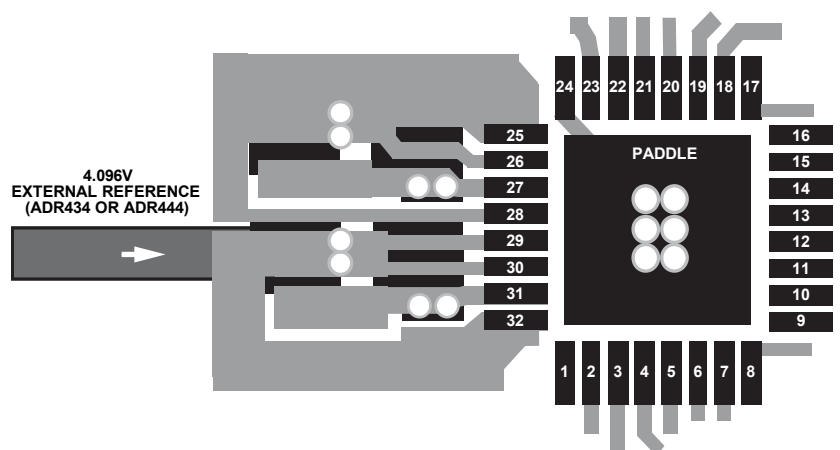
ピン 24~ピン 32 に対する推奨 PCB レイアウトとデカップリング
